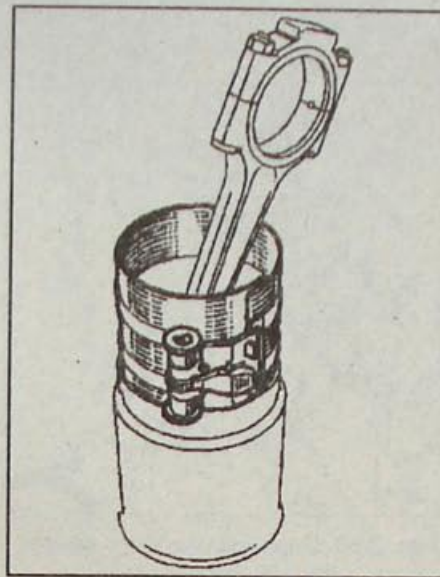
Использование приспособления для сжатия поршневых колец при установке поршня с шатуном в гильзу цилиндра
